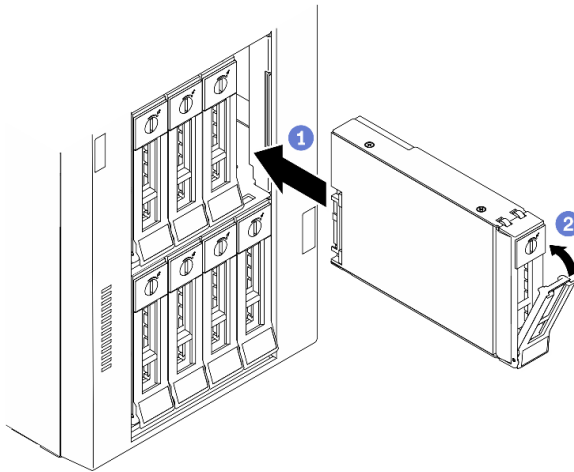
Installation d'unité à remplacement standard 3,5 pouces
